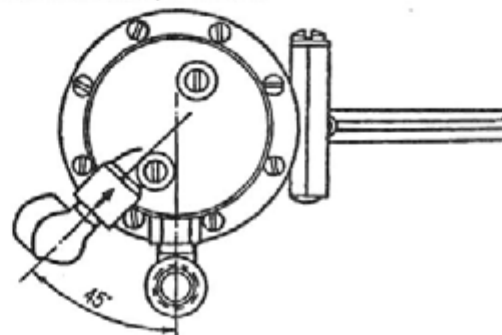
Положение головки и крышки топливного насоса относительно корпуса
